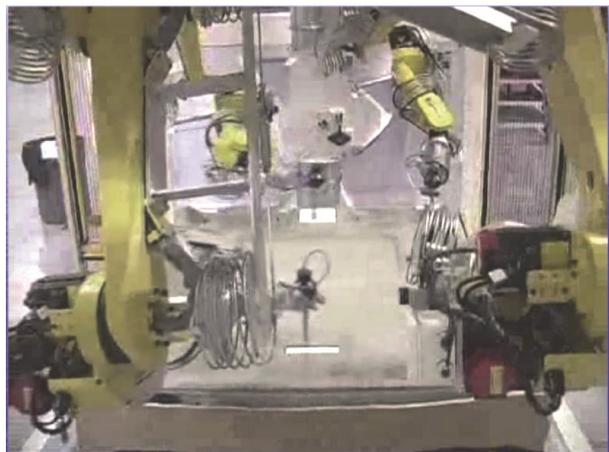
Фрезерно-сверлильная обработка детали четырьмя роботами
